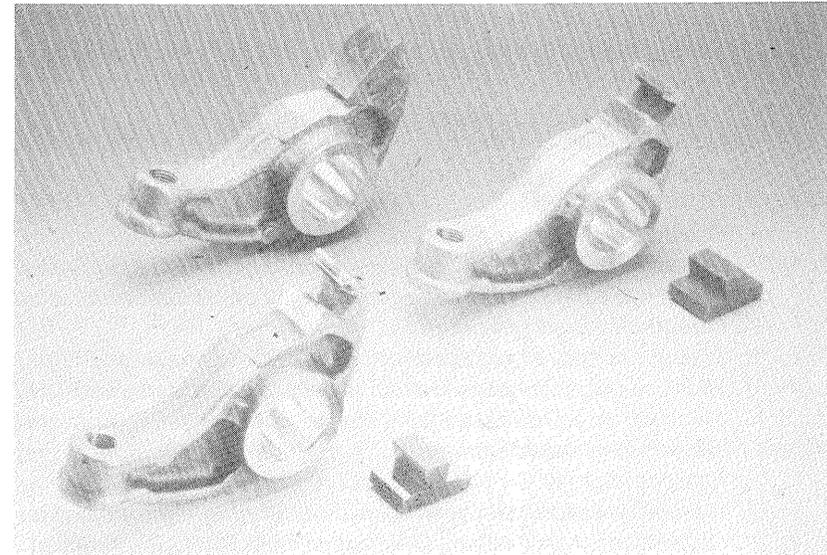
Kipphebel mit Sintermetalleinsätzen
